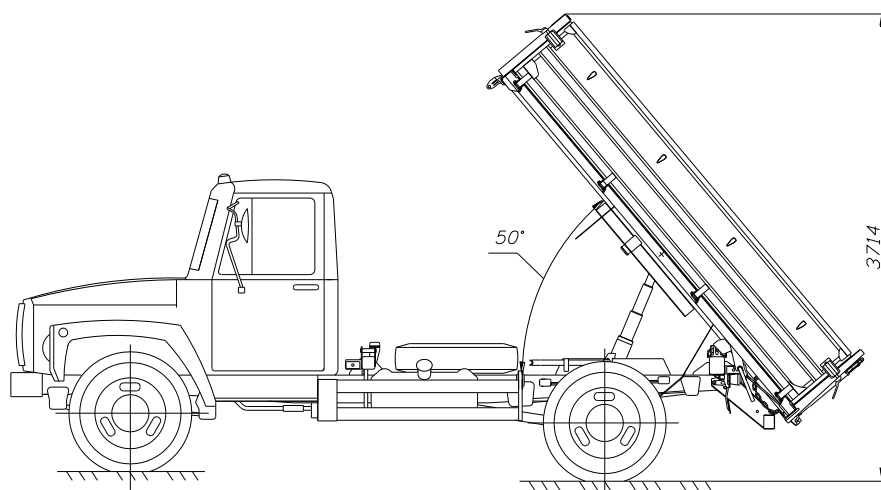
Основные размеры автомобиля-самосвала в рабочих положениях.
